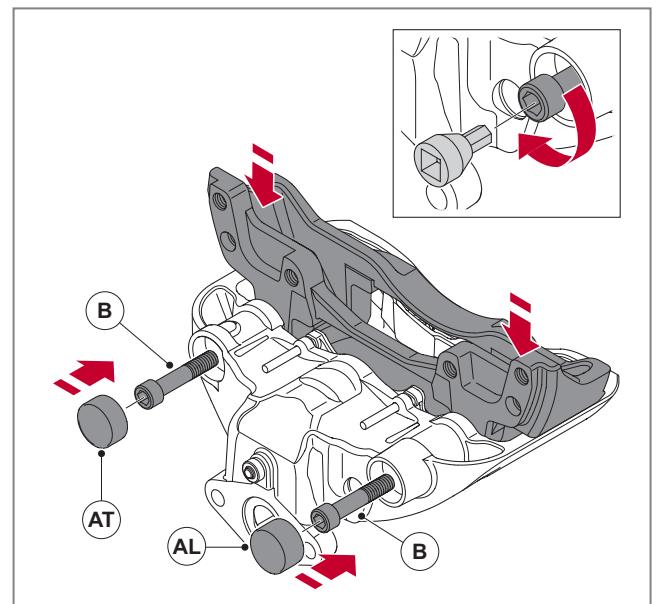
Bremsträger und Befestigungsschrauben wieder anbringen
